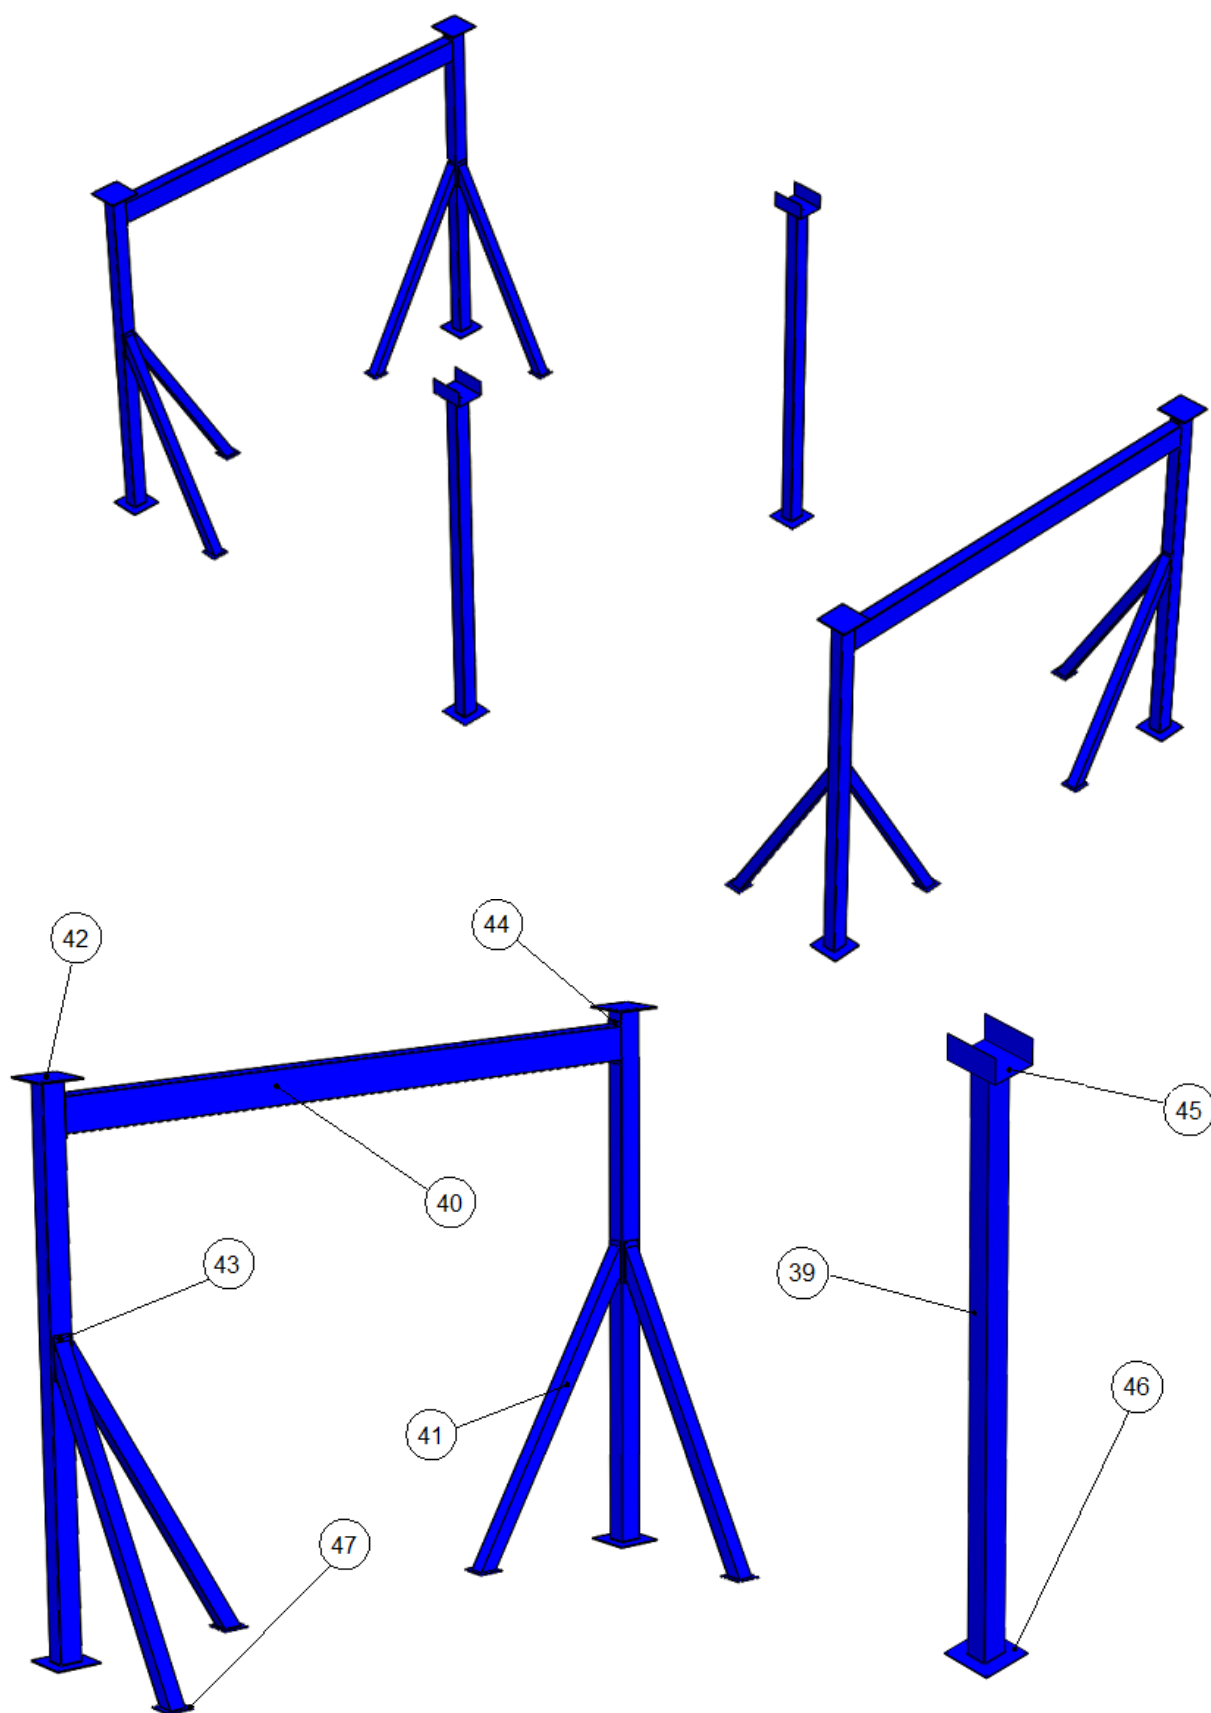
CAD completo y detalle de la estructura soporte.
